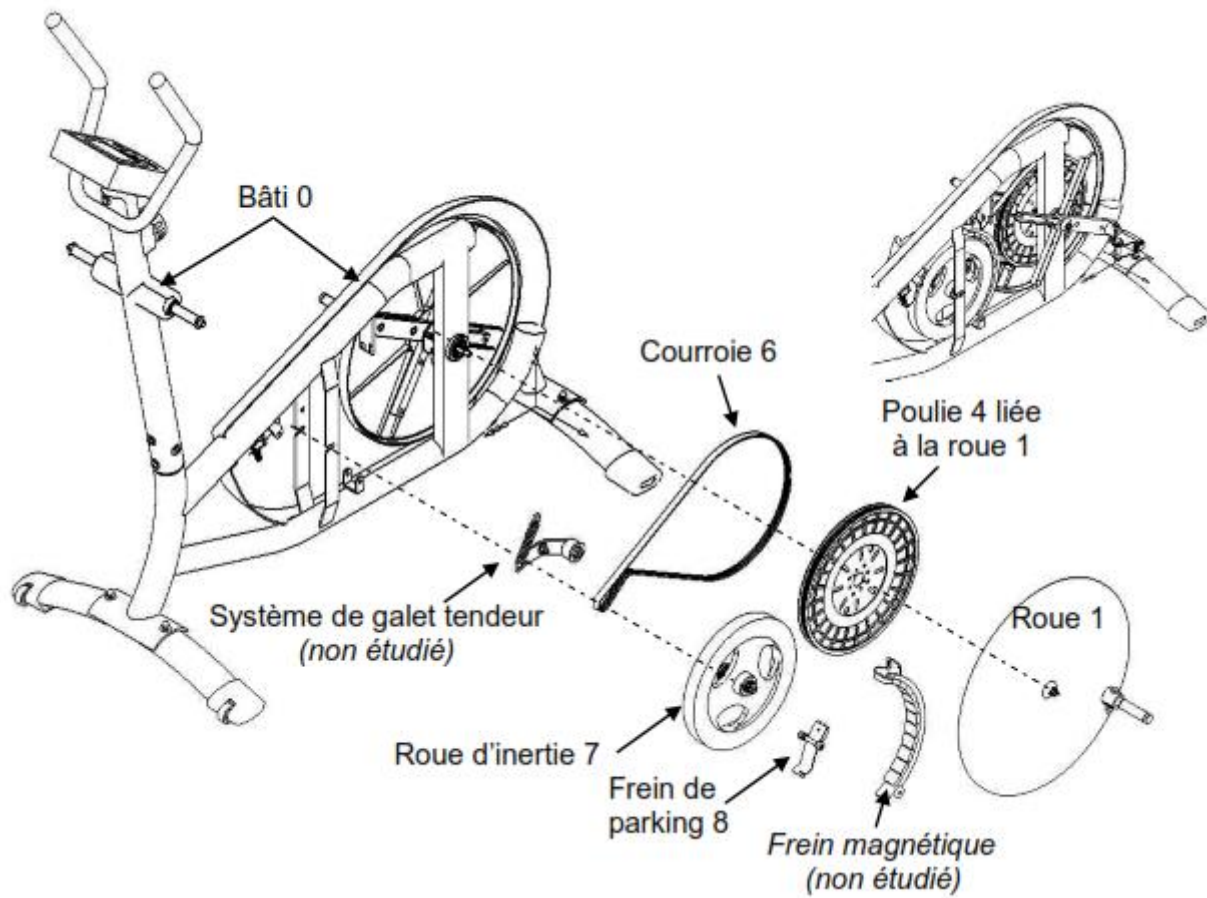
Vue éclatée des sous-ensembles extérieurs
